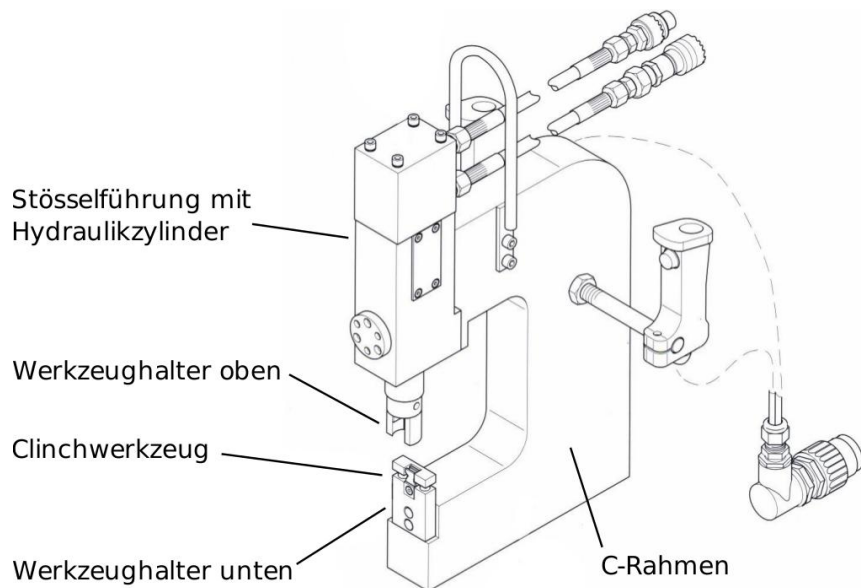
Clinchmaschine mit hydraulischem Antrieb. Teile: Stößelführung mit Hydraulikzylinder, Werkzeughalter oben; Clinchwerkzeug; Werkzeughalter unten; C-Rahmen
